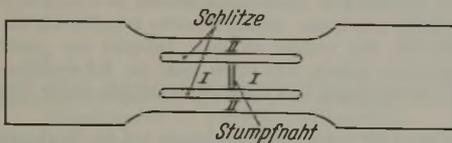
Geschweißter Probestab für Zugversuche zur Beobachtung des Spannungsabbaus.
